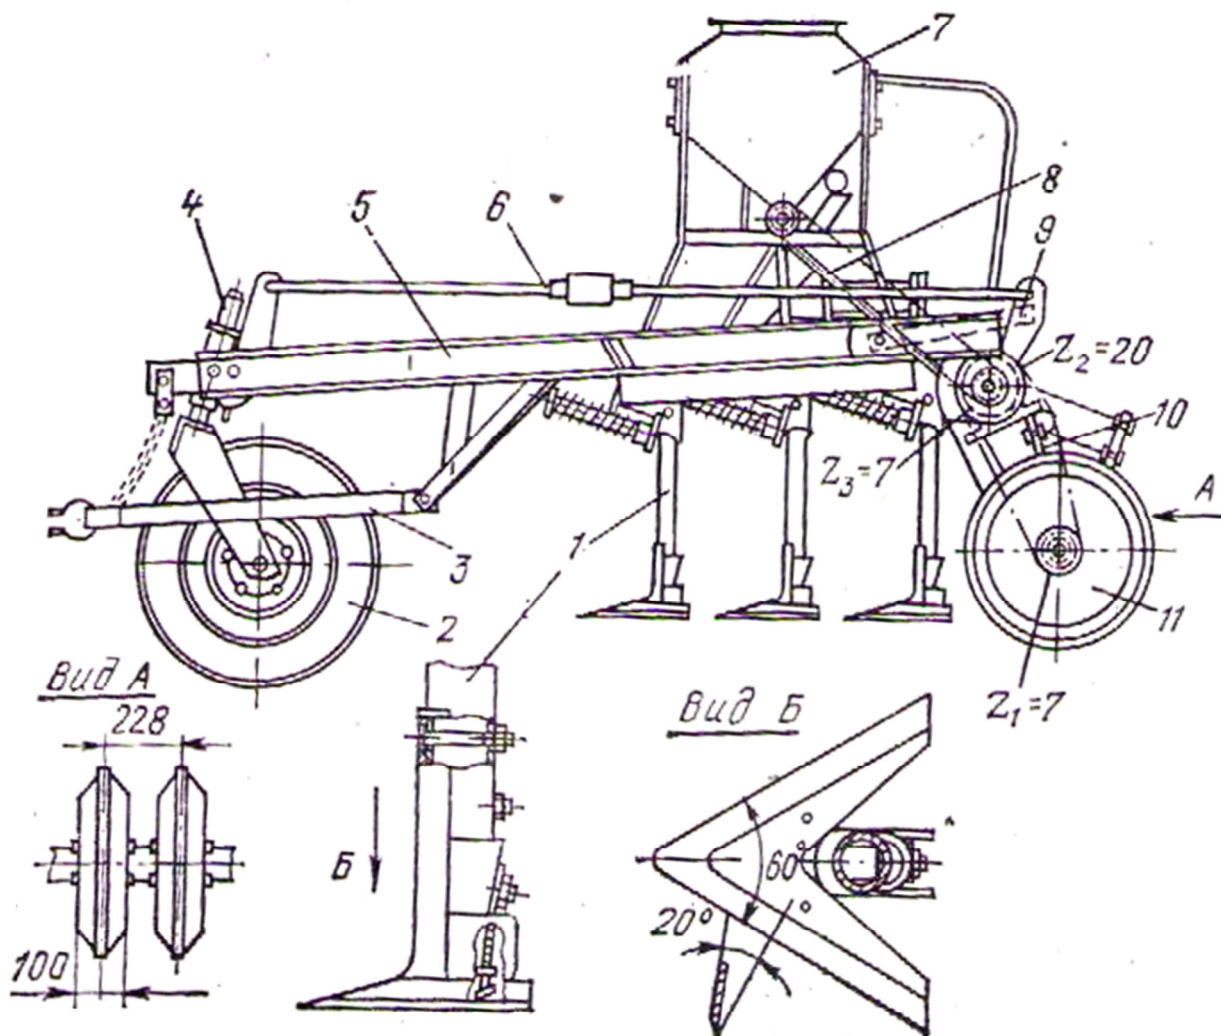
Сеялка СЗС-2,1: 1 - сошник; 2 - колесо опорное; 3 - устройство прицепное; 4 – ось вилки опорного колеса; 5 - рама; 6 - тяга длинная; 7 - ящик зернотуковый; 8 - устройство гидравлическое; 9 - планка транспортная; 10 - кронштейн; 11 - прикатывающие катки.
